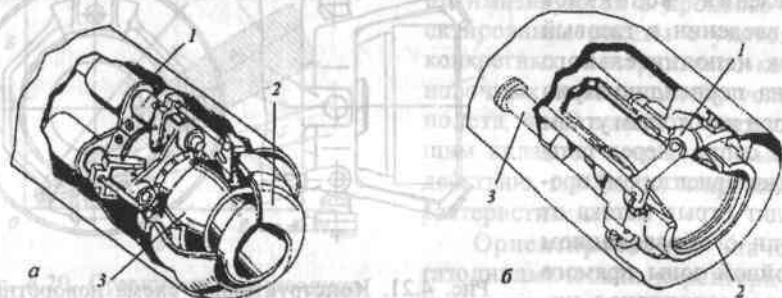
Конструктивные схемы СУВТ с поворотными исполнительными органами:
